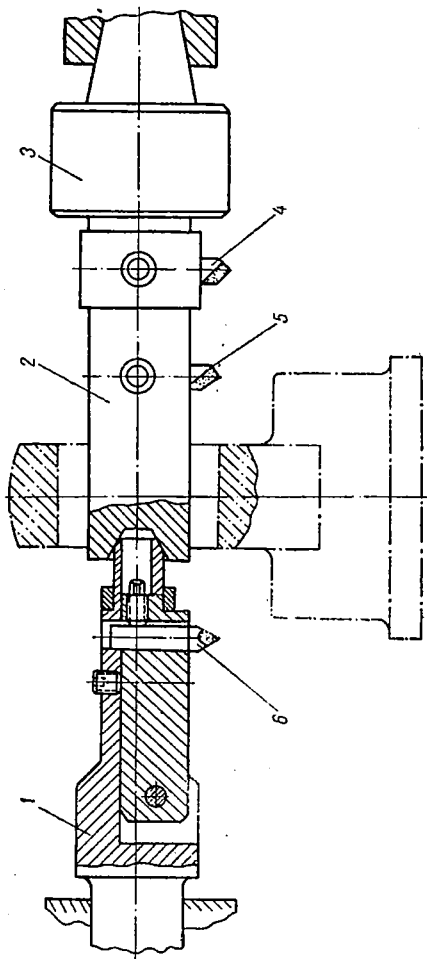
Приспособление для черновой и чистовой расточки отверстий.
